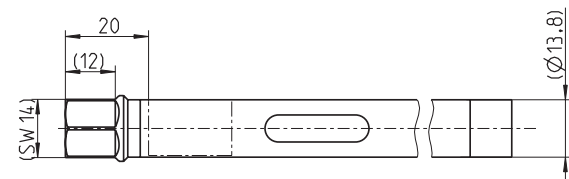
Montageschlüssel ø13,8/SW14 Typ 1300A67 für Einbaubohrung ø14 mm
